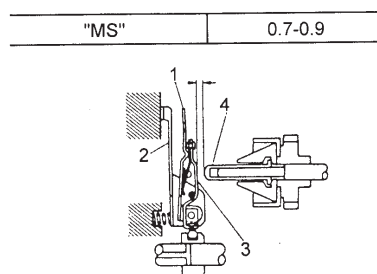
Установочный размер «MS»: 1 - силовой рычаг, 2 - регулировочный рычаг, 3 - нажимной рычаг, 4 - сменный наконечник муфты.
